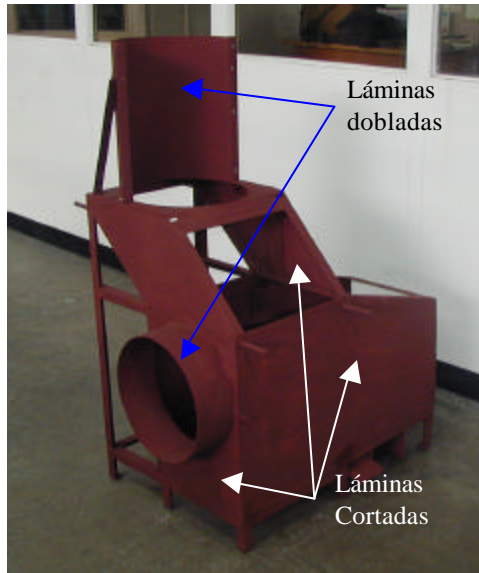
Estructura de trabajo parcialmente cubierta con su carcasa.
